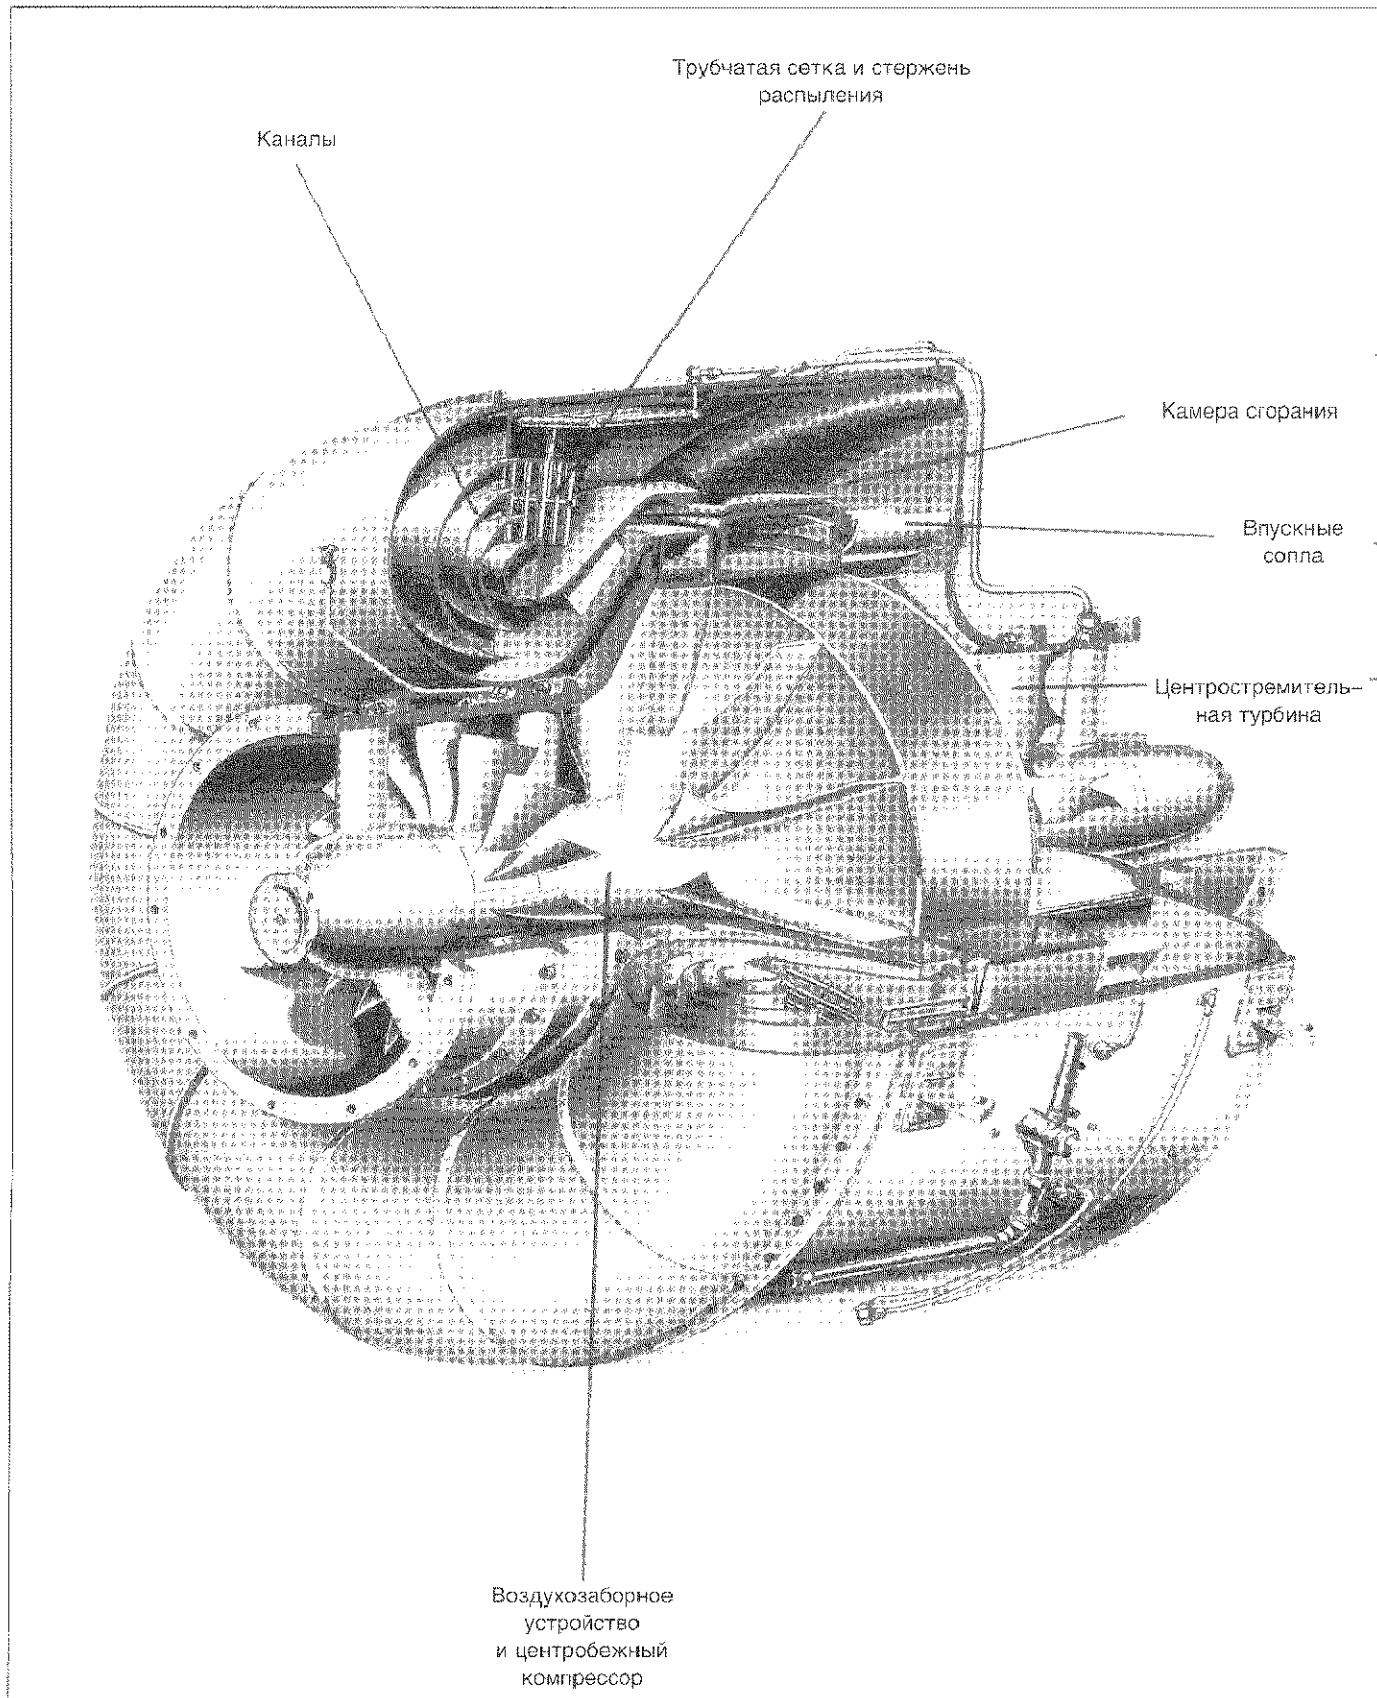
Турбореактивный двигатель HeS 3b (схема получена от Билла Ганстона)
